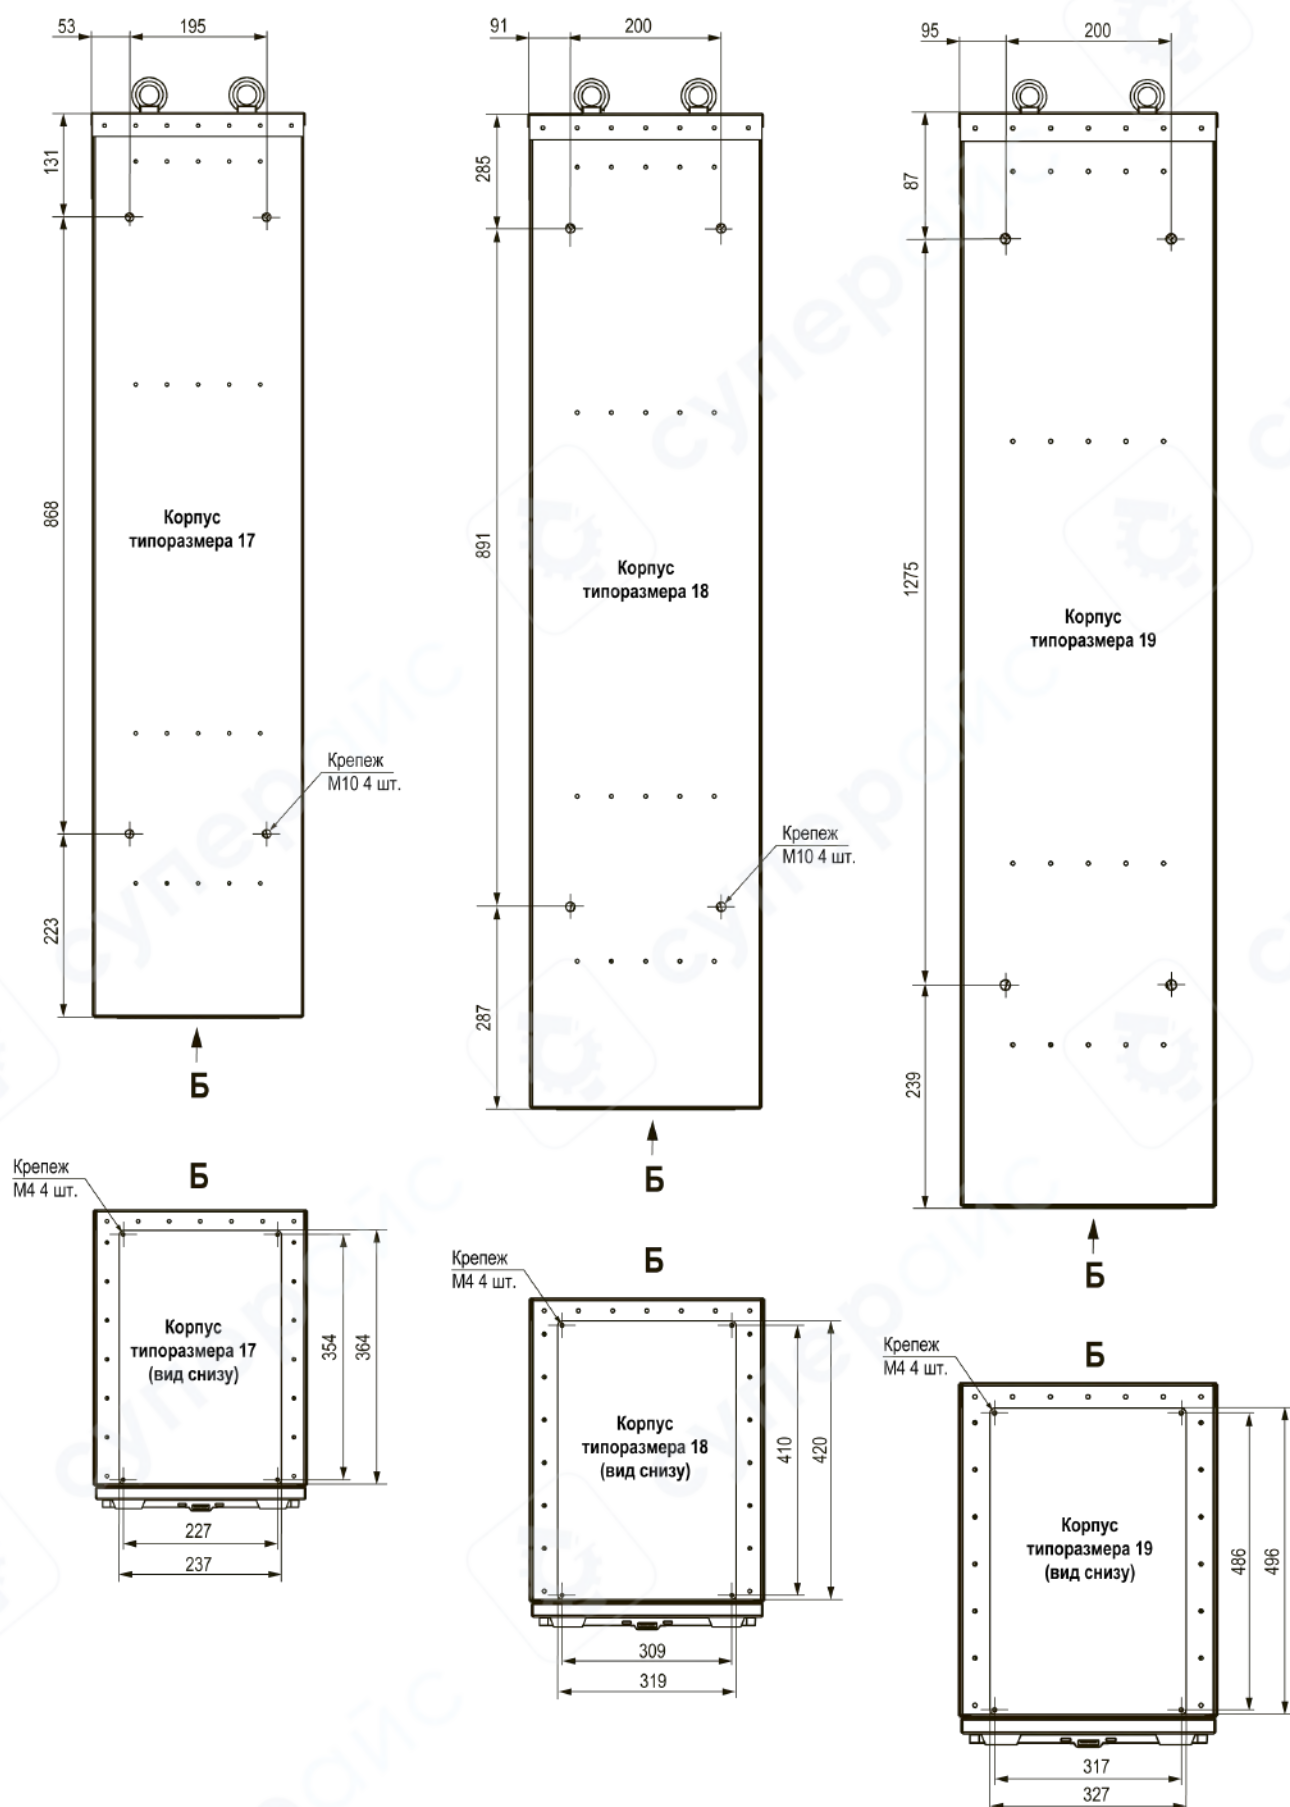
Присоединительные размеры для корпусов типоразмеров 17–19
